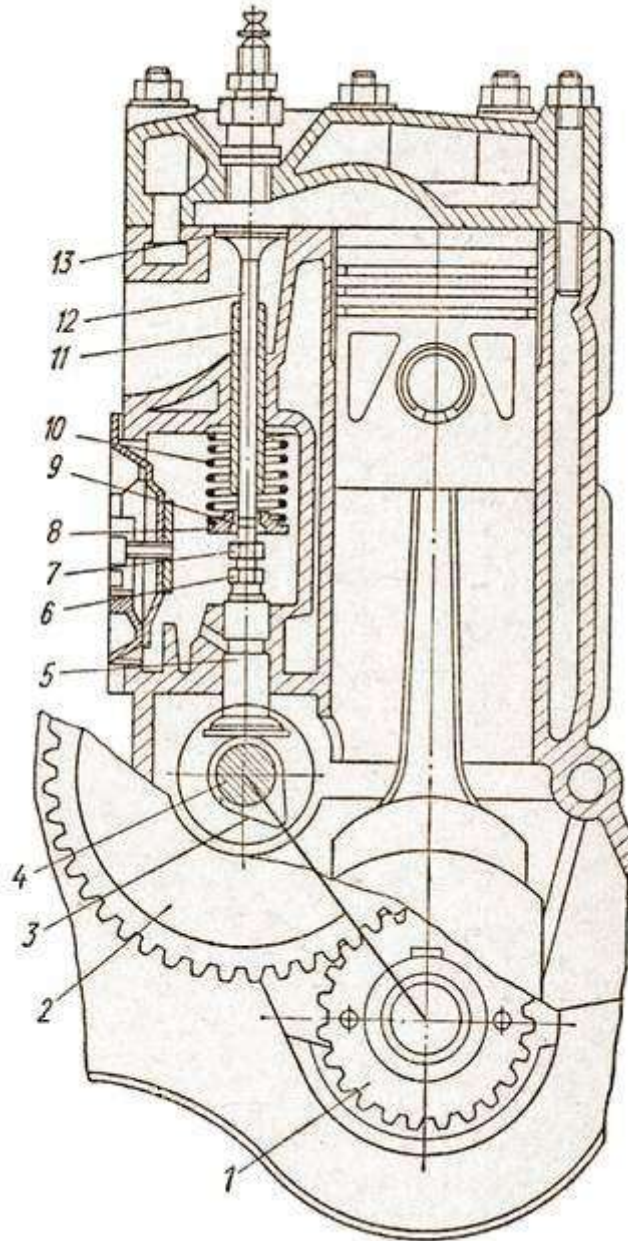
Газорозподільний механізм з нижнім розташуванням клапанів
